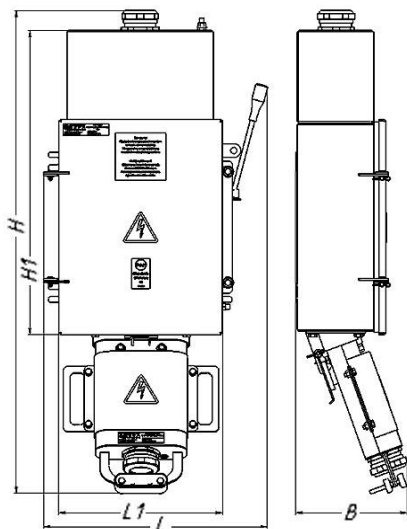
Общий вид и габаритные размеры ВРН-Ш/Р(Twin)
